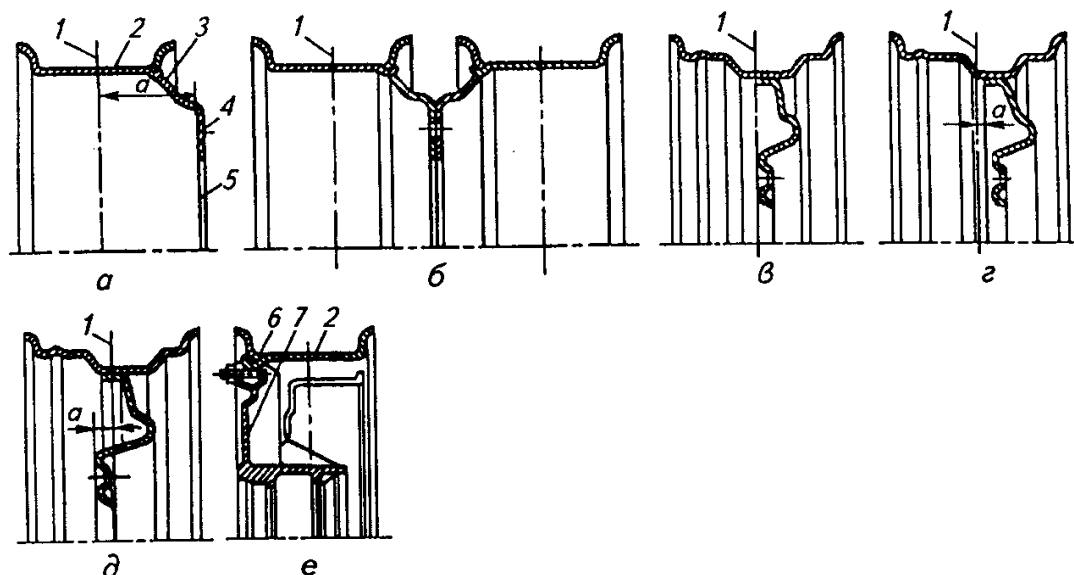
Конструктивные схемы колес: *а* — одинарного; *б* — сдвоенного; *в, г, д* — с различными вылетами диска; *е* — бездискового; 1 — вертикальная ось колеса; 2 — обод; 3 — диск; 4 — крепежные отверстия; 5 — центральное отверстие диска; 6 — элементы крепления; 7 — ступица
